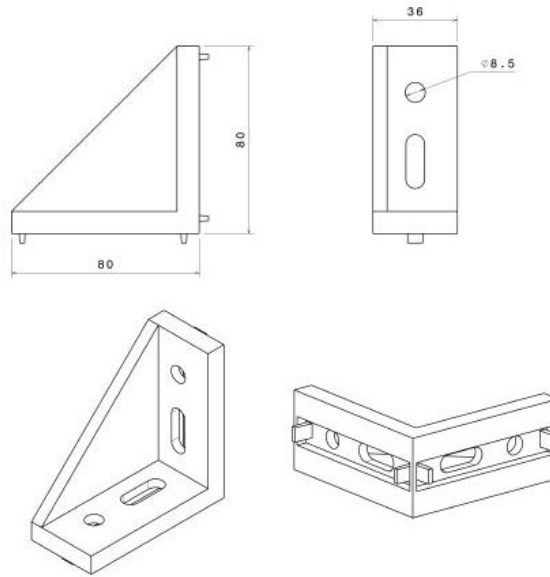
Dimensiones escuadra de fundición de aluminio para perfil de aluminio de 40x40 mm
